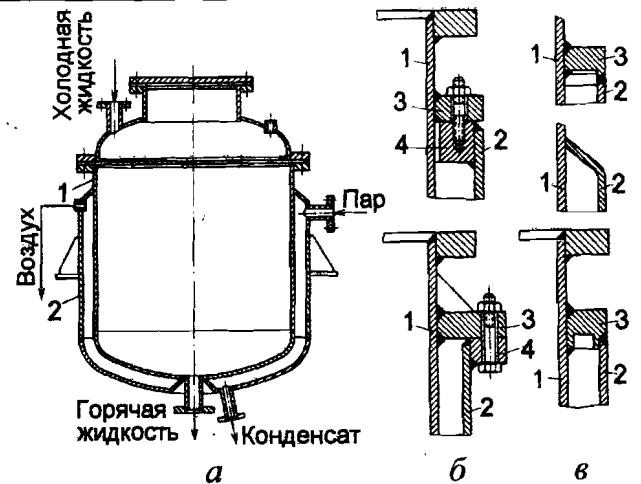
Аппарат с греющей рубашкой (а) и способы ее присоединения (б – фланцевое; в – сварное):
